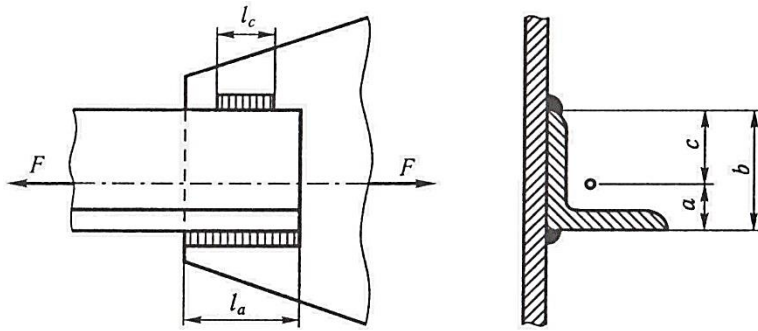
Схема до розрахунку зварювального шва кутника
